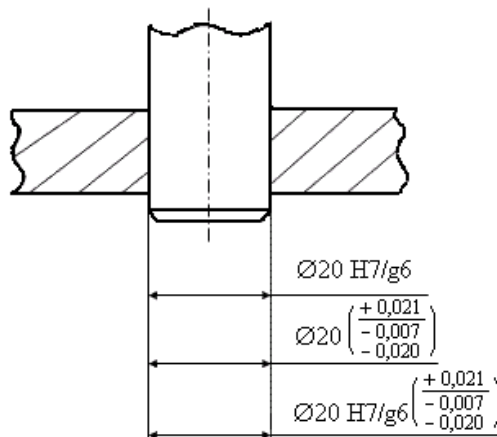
Обозначение посадки на сборочном чертеже различными способами
